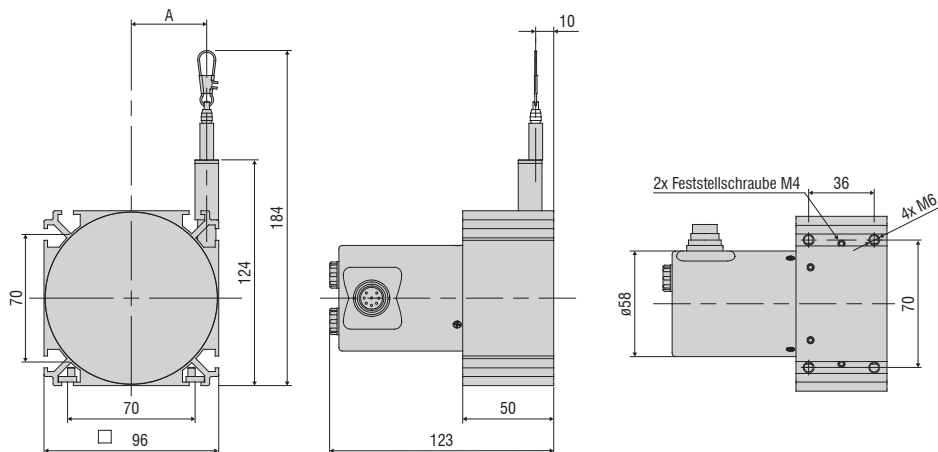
Maßzeichnung WDS- ... - P96 - SR - U/I, Abmessungen in mm
